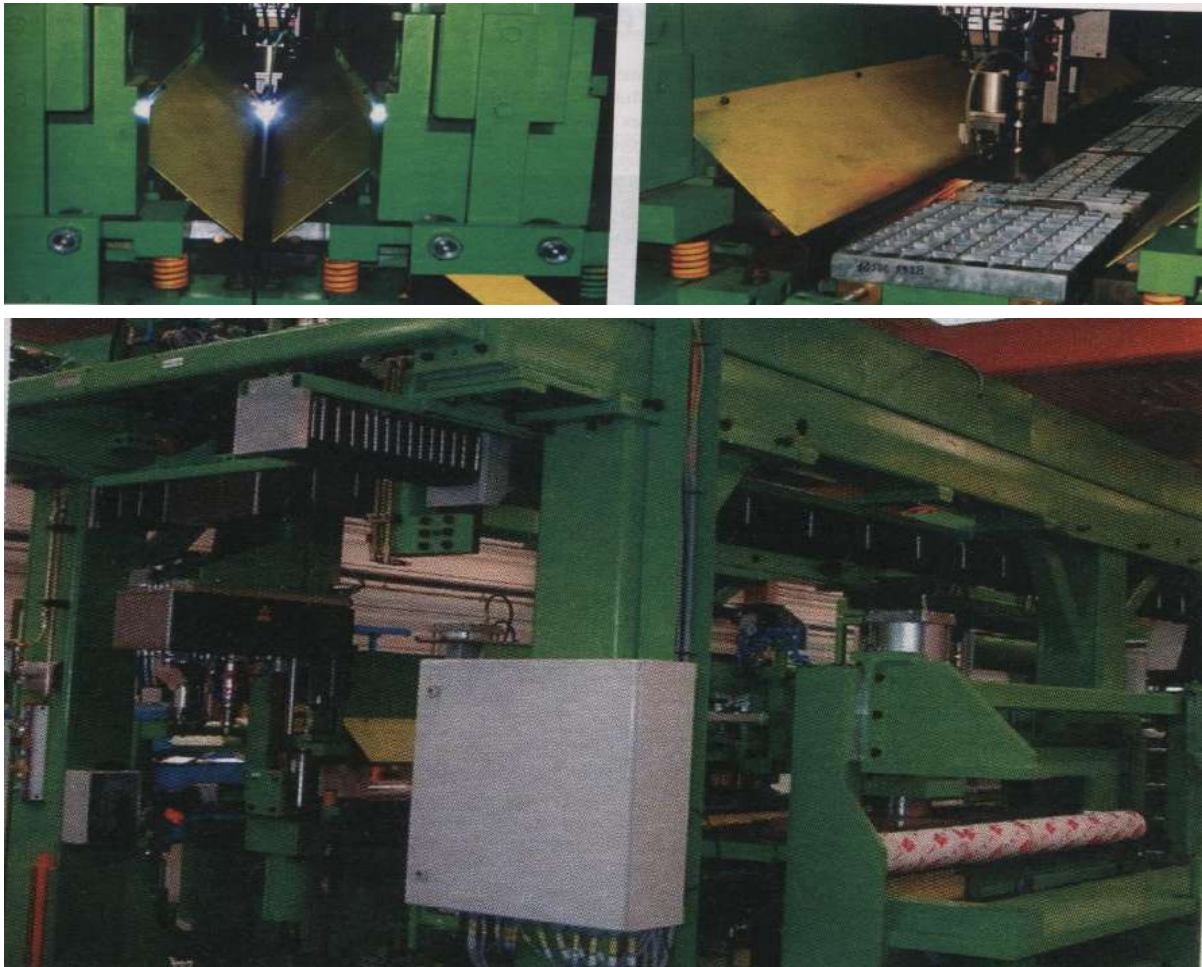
Лазерні машини для стикового зварювання фірми *IDEAL
